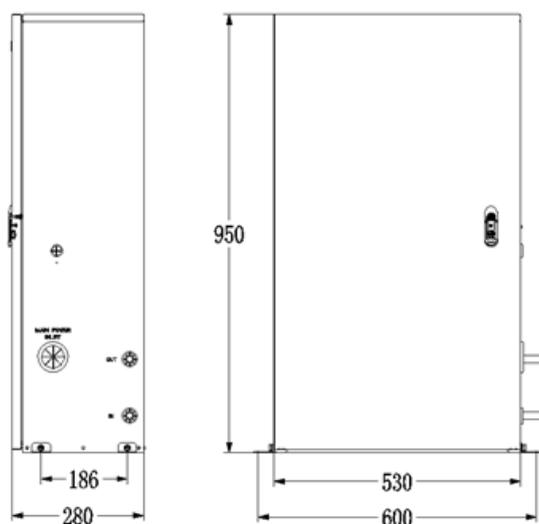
Габаритные размеры энергосберегающего модуля фторопластового насоса
